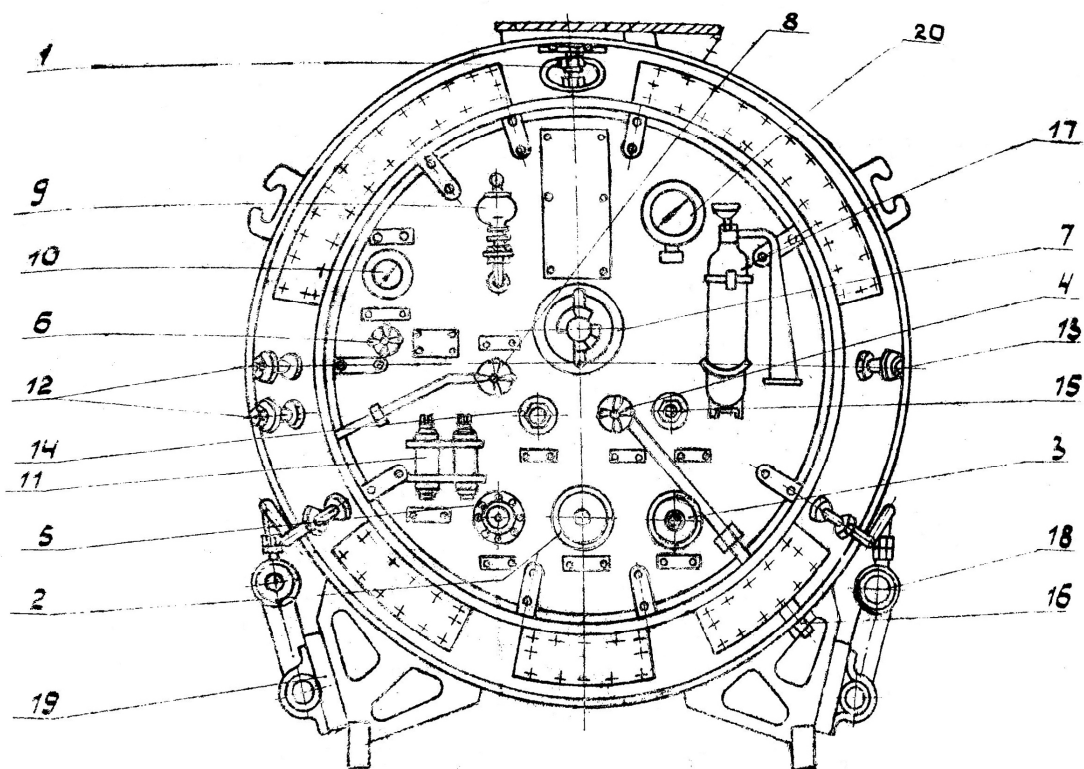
Схема передней крышки резервуара ТРЖК-7М:
